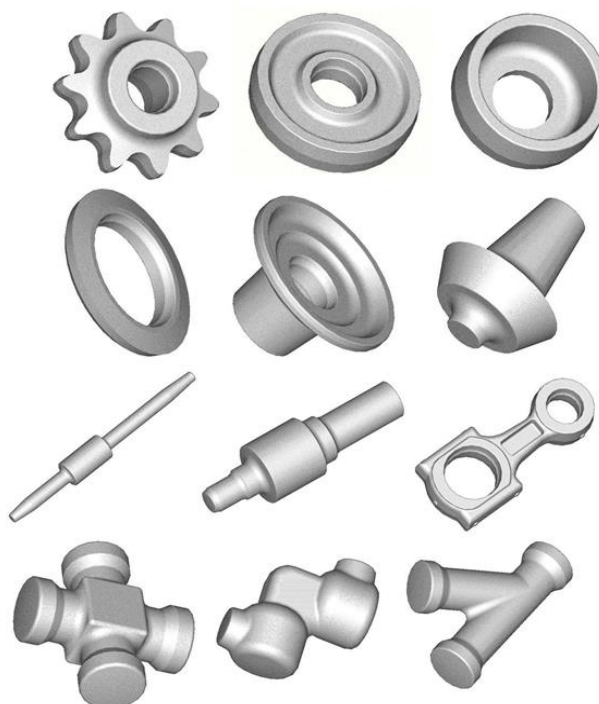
Форми поковок, що виготовляються об’ємною штамповкою
